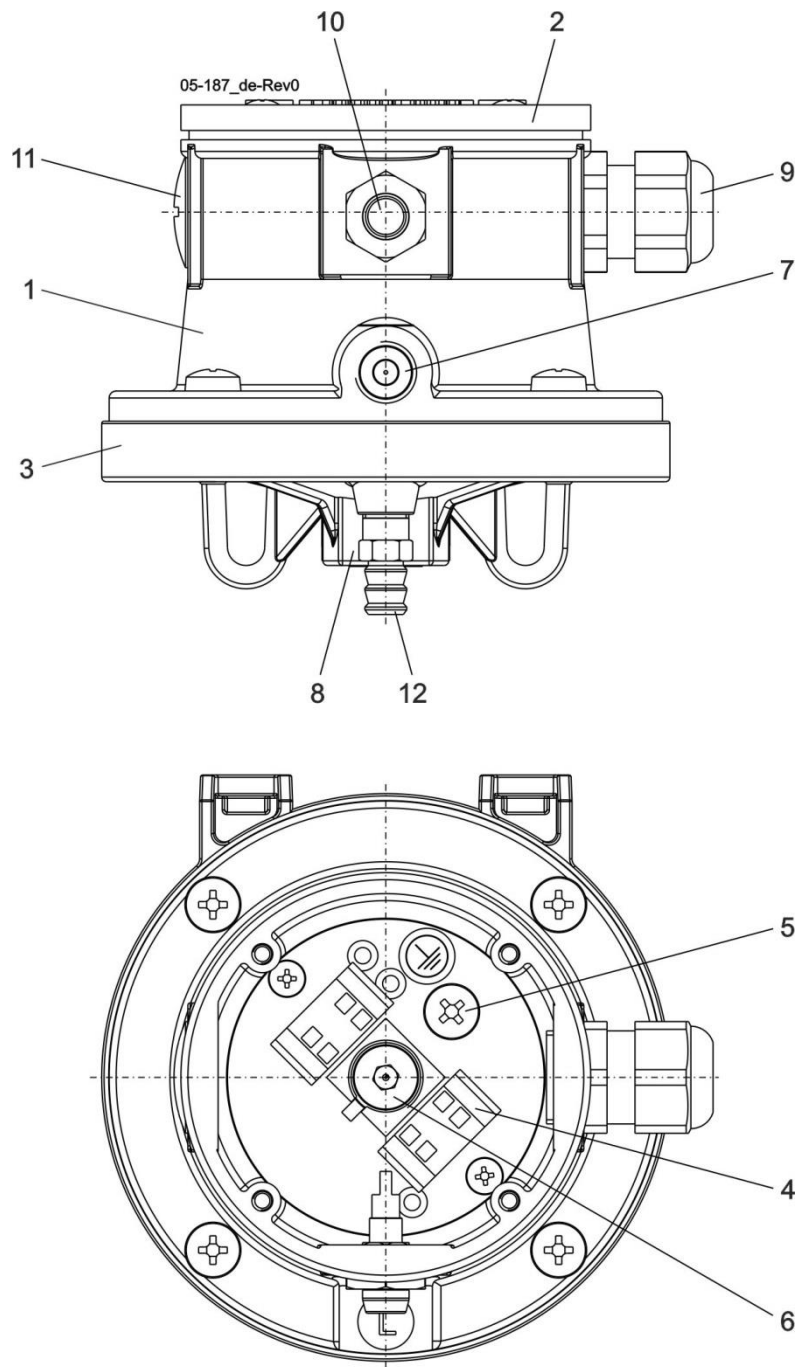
Druckwächter (Ausführung mit Signallampe und Kabelverschraubung, Draufsicht auf Anschlussraum)
